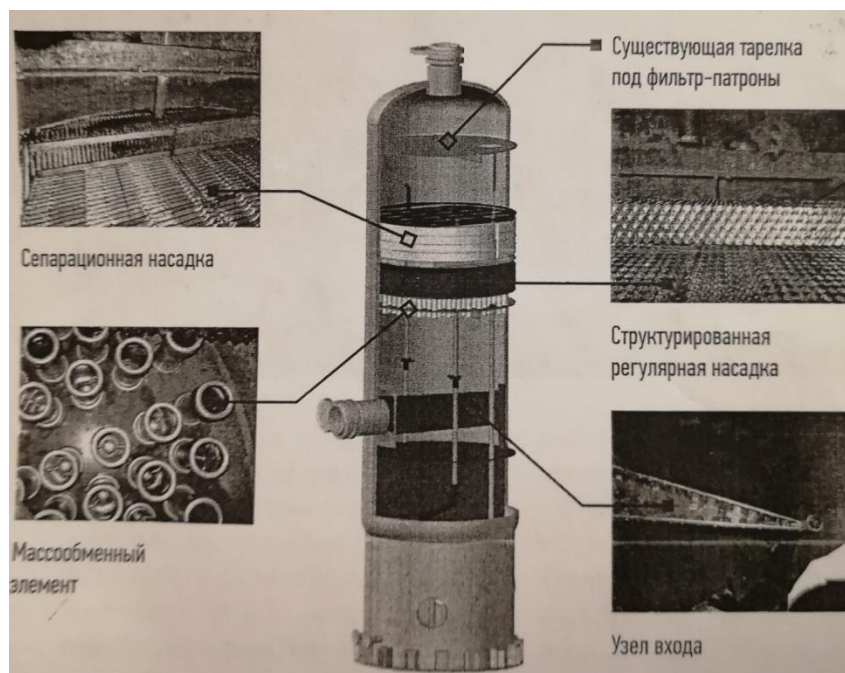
Модернизированный сепаратор с промывочной секцией цеха очистки газа Юбилейного НГКМ [3]
